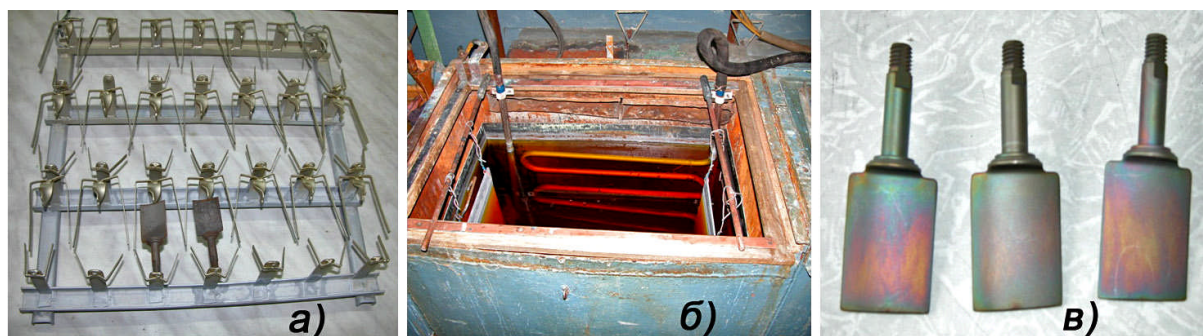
Оборудование для нанесения гальванических покрытий: а – держатель лопаток компрессора; б – гальваническая ванна; в – лопатки компрессора с никель-кадмиевыми покрытиями
